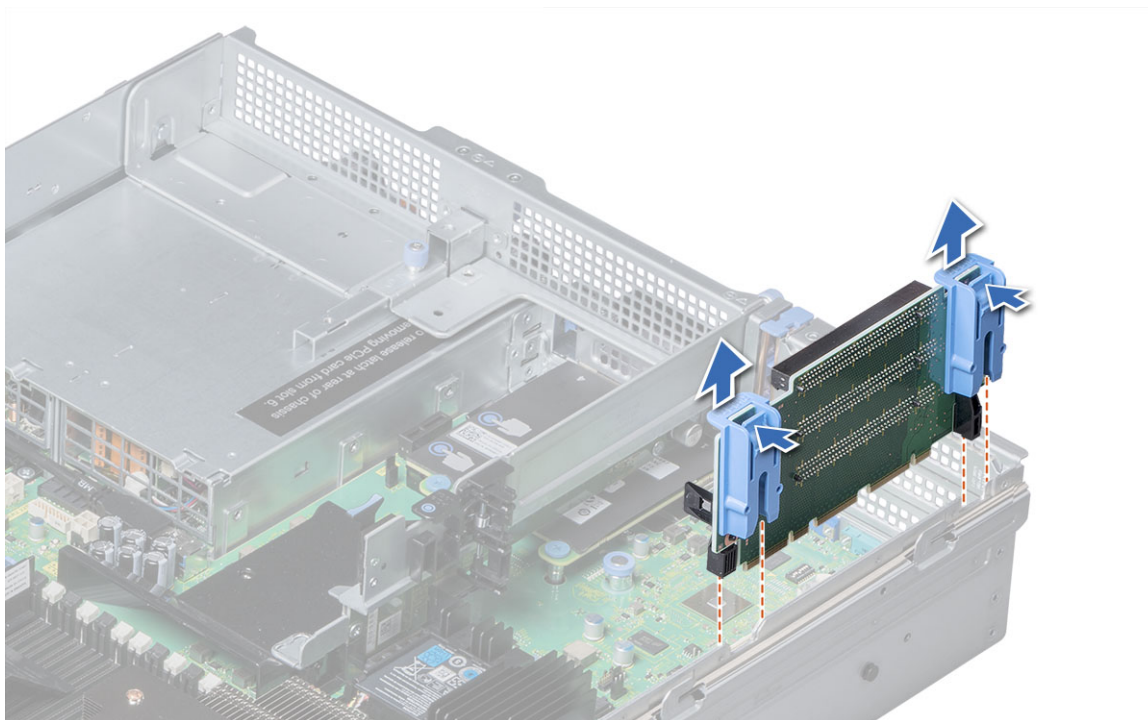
Retrait de la carte de montage 1 pour carte d'extension
